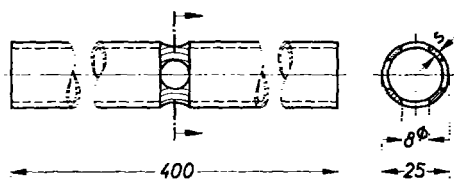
Rohr-Kerbzugprobe mit 4 Bohrungen
